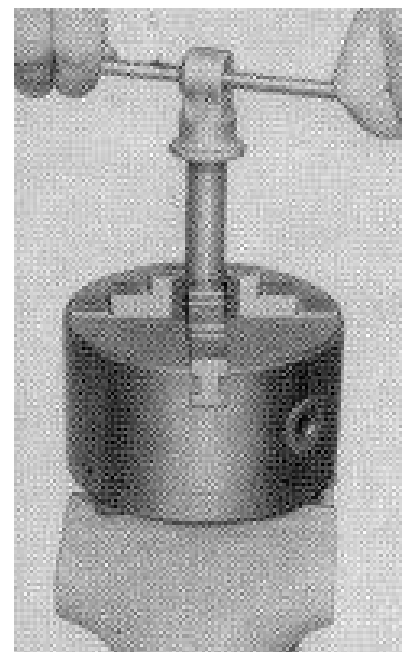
Kolbenstange ins Dreibackenfutter spannen
